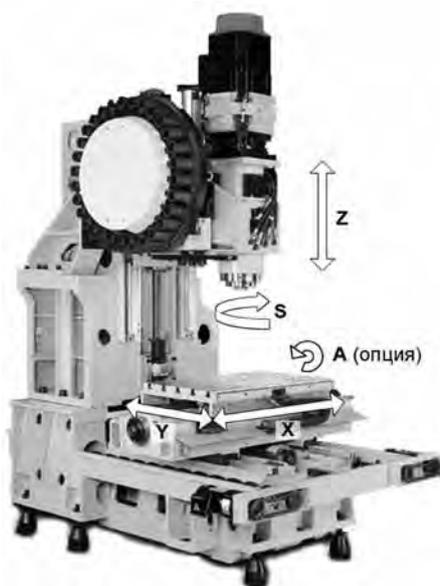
Вертикально-фрезерный многоцелевой обрабатывающий центр Quaser MV 184P
